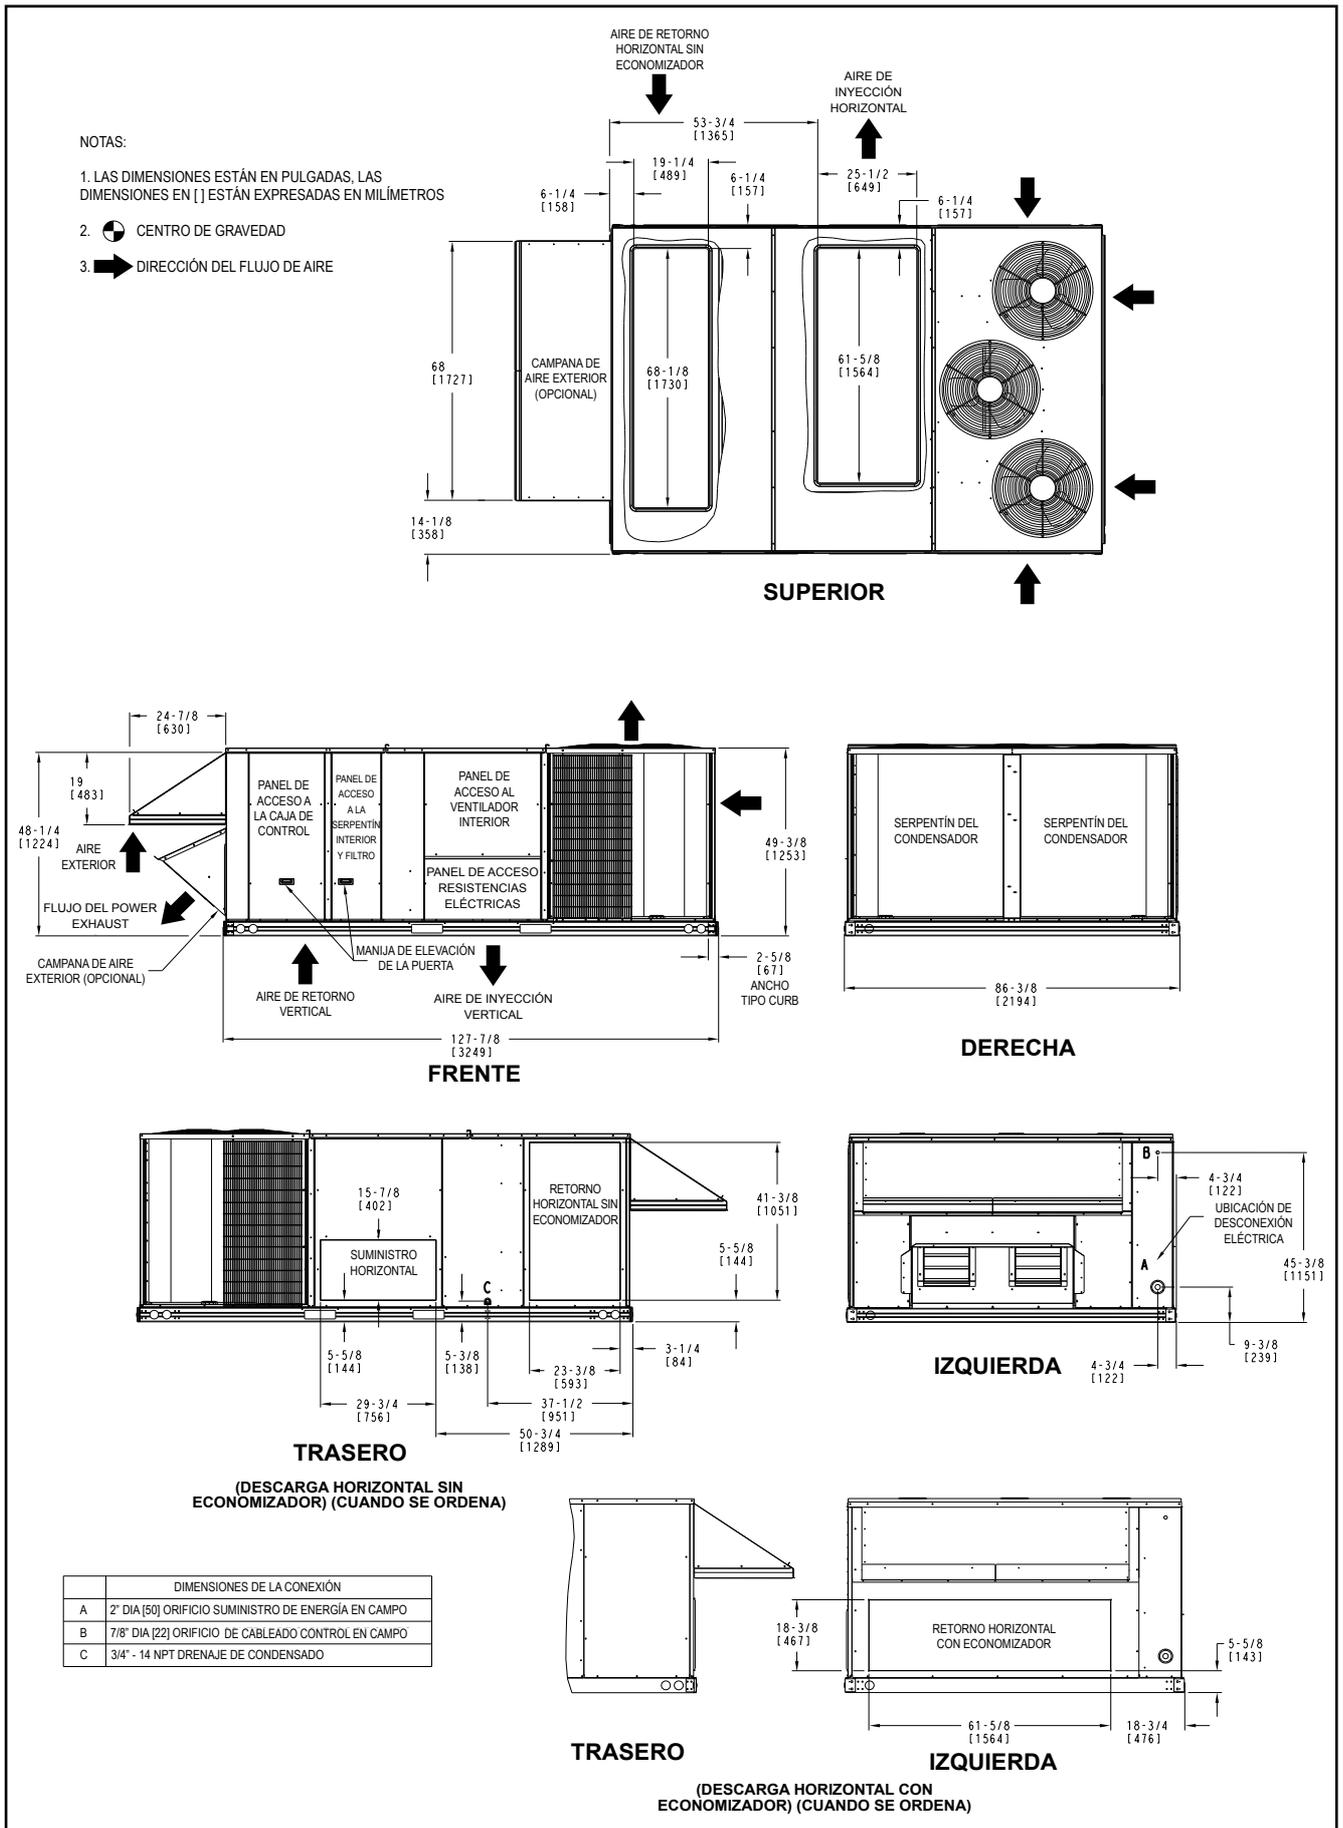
Dibujo dimensional de la unidad - 652EZ210
